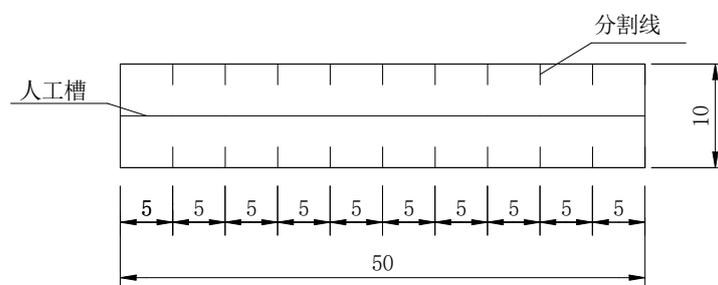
12 C 型灵敏度试片的尺寸 (mm)
